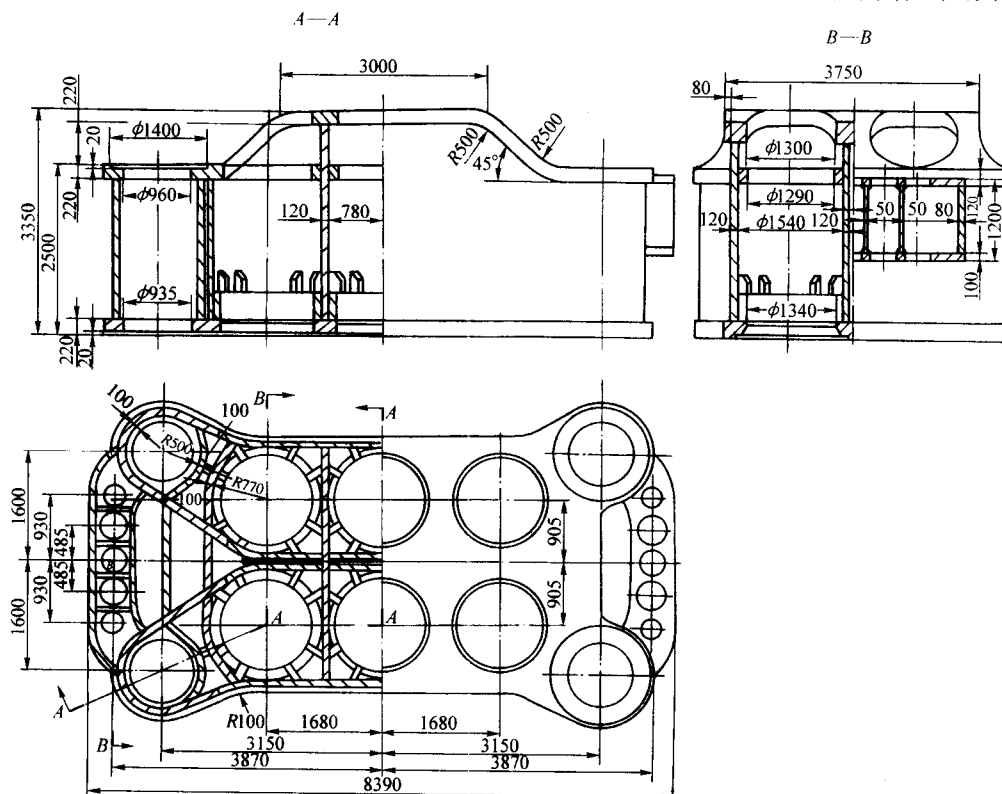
120 MN 水压机上横梁的焊接结构
